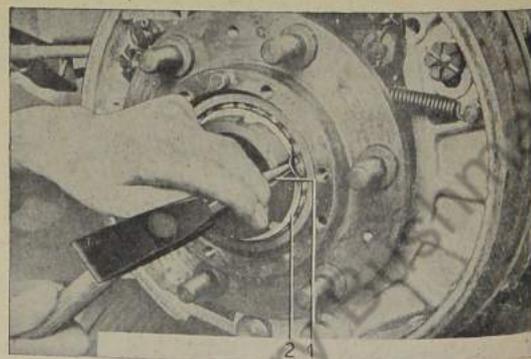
Sicherungsblech für Nutmutter aufbiegen
